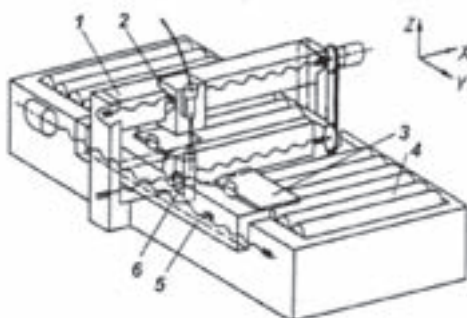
Компоновка установки водоструйной резки с неподвижным порталом.
